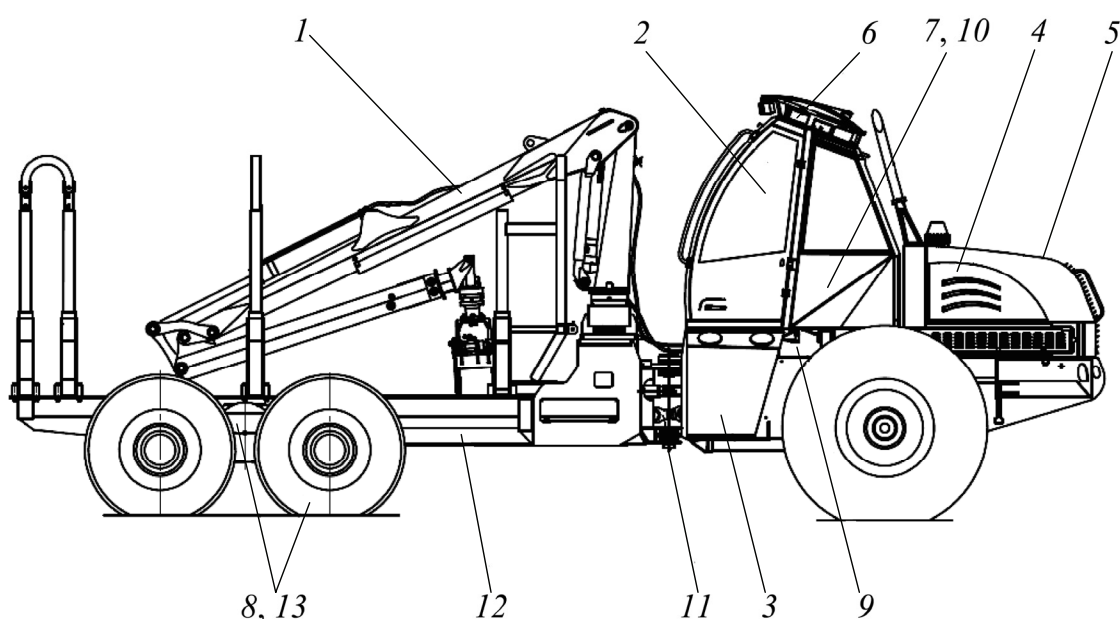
Общий вид форвардера «Амкодор 2661-01»:
